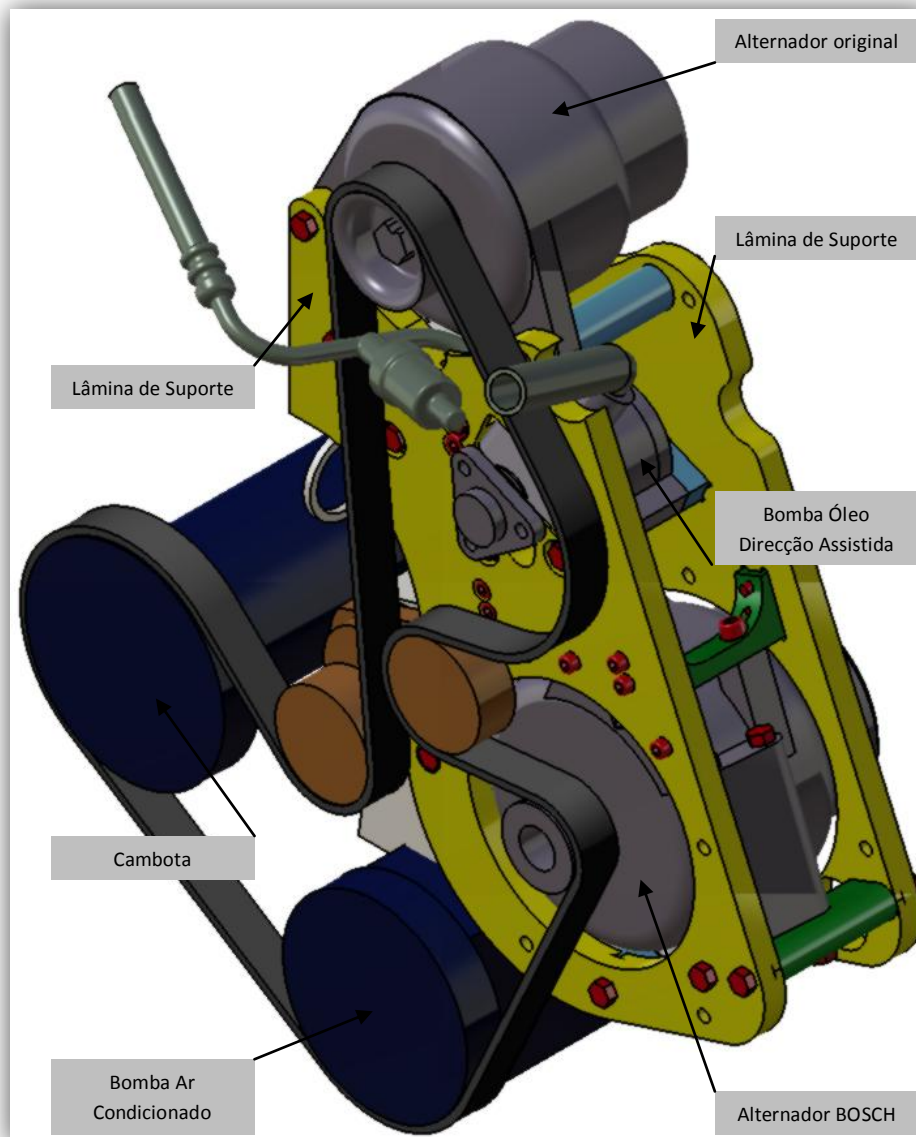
CAD 3D da solução para a colocação do alternador BOSCH
